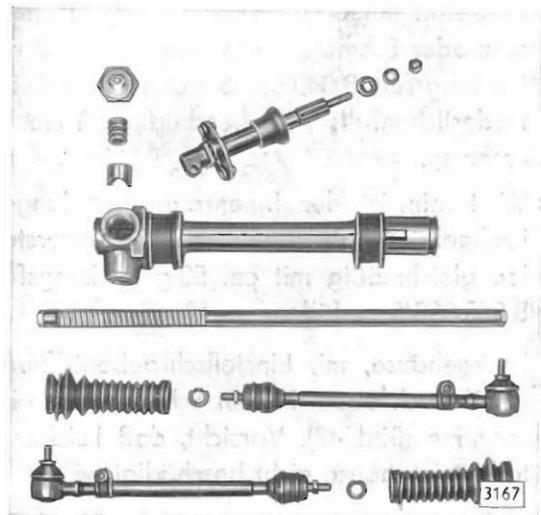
Lenkgetriebe mit Spurstangen zerlegt
